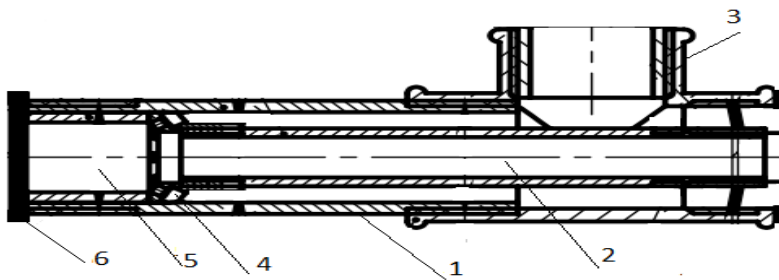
Загальний вигляд розробленого пінозмішувача: 1 – циліндричний корпус; 2 – канал для подавання водного розчину піноутворювача; 3 – канал для подавання повітря під тиском; 4 – знімний реактор; 5 – камера піноутворення; 6 – пакети сіток
